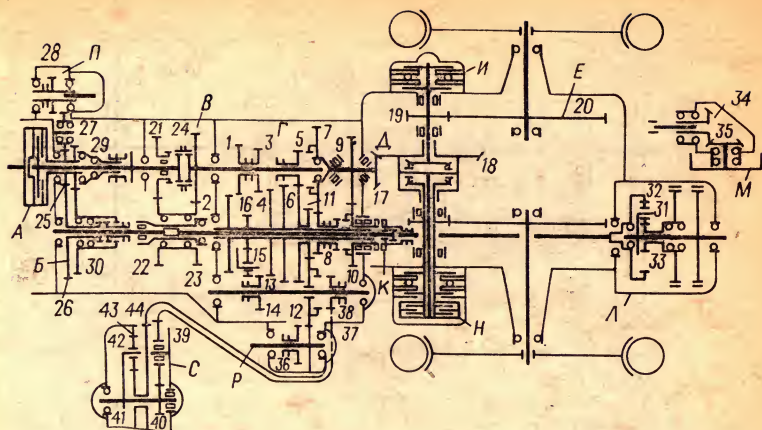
Кинематическая схема силовой передачи трактора МТЗ-80: А — муфта сцепления; Б — двухскоростной редуктор привода ВОМ; В — редуктор-удвоитель числа передач; Г — коробка передач; Д — центральная передача с дифференциалом; Е — конечная передача; И — дисковый тормоз; К — зубчатая муфта переключения ВОМ на независимый и синхронный привод; Л — планетарный редуктор ВОМ; М — приводной шкив; Н — муфта блокировки дифференциала, управляемая от гидросилителя руля; П — привод к насосу навесной системы; Р — привод бокового ВОМ; С — ходоуменьшитель
